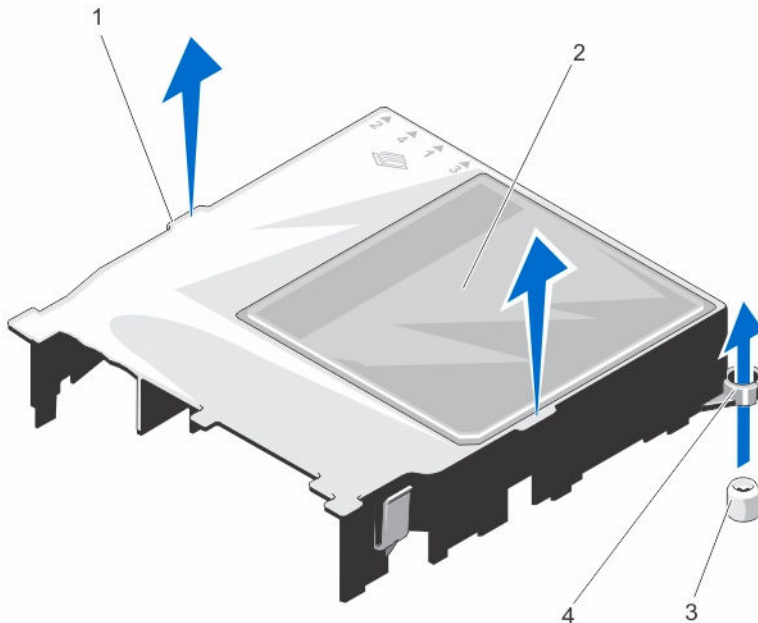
Entfernen und Einsetzen des Kühlgehäuses
